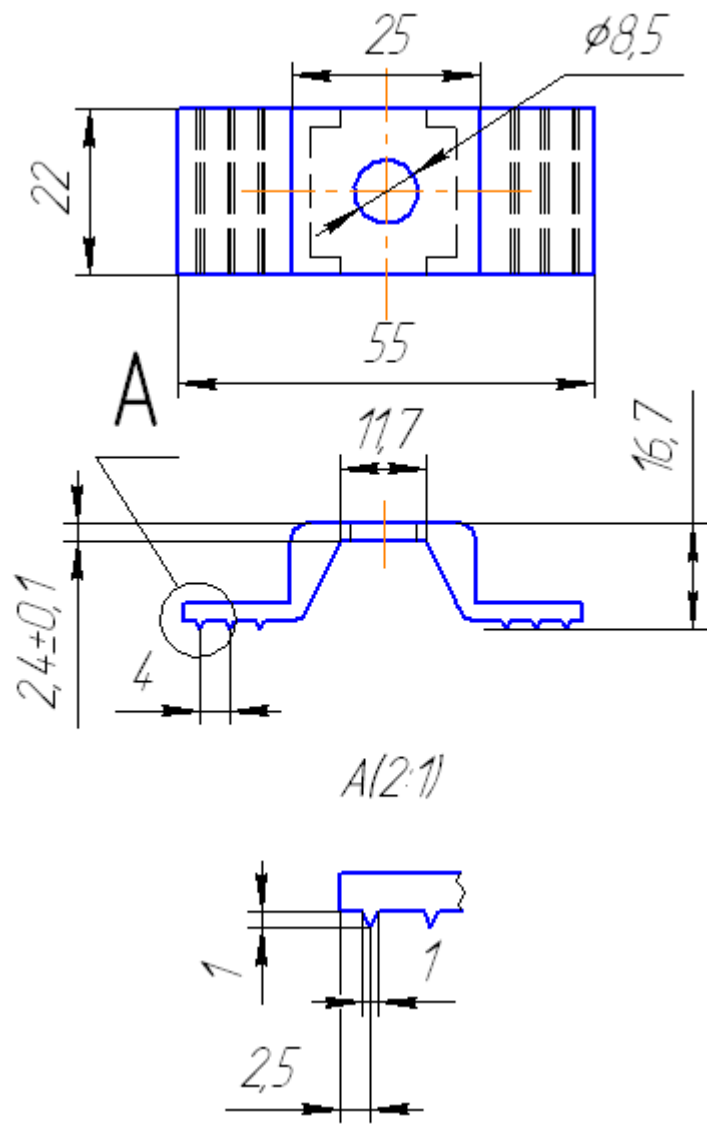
Чертеж детали «Кронштейн обивки двери передней»
